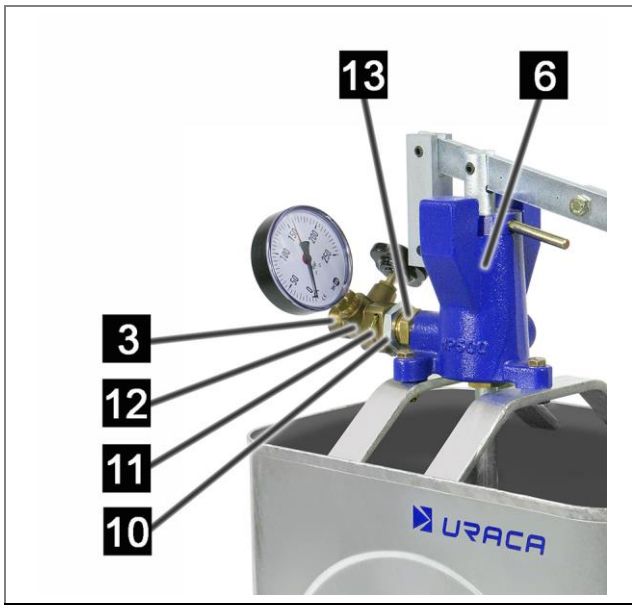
Ausbau Druckventil Handprüfpumpe HP300
